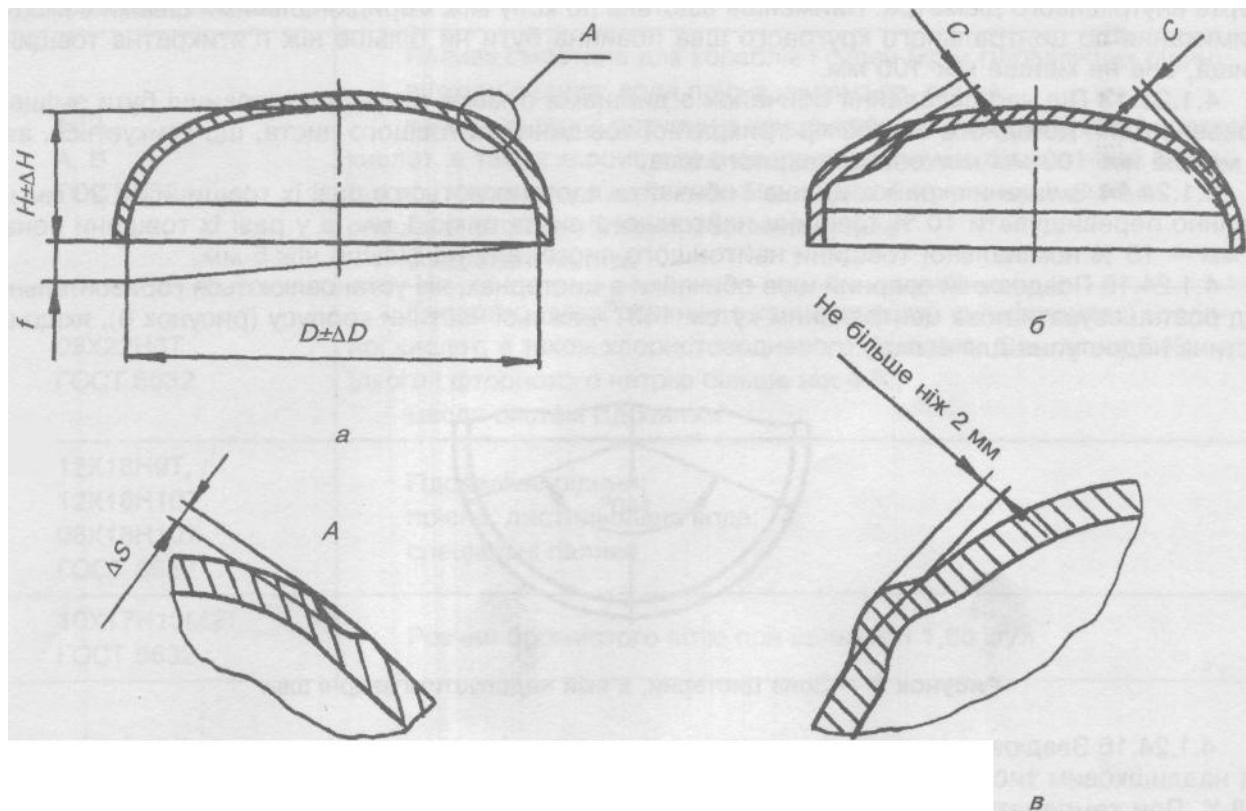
Види і допуски відхилень від геометричної форми днищ
